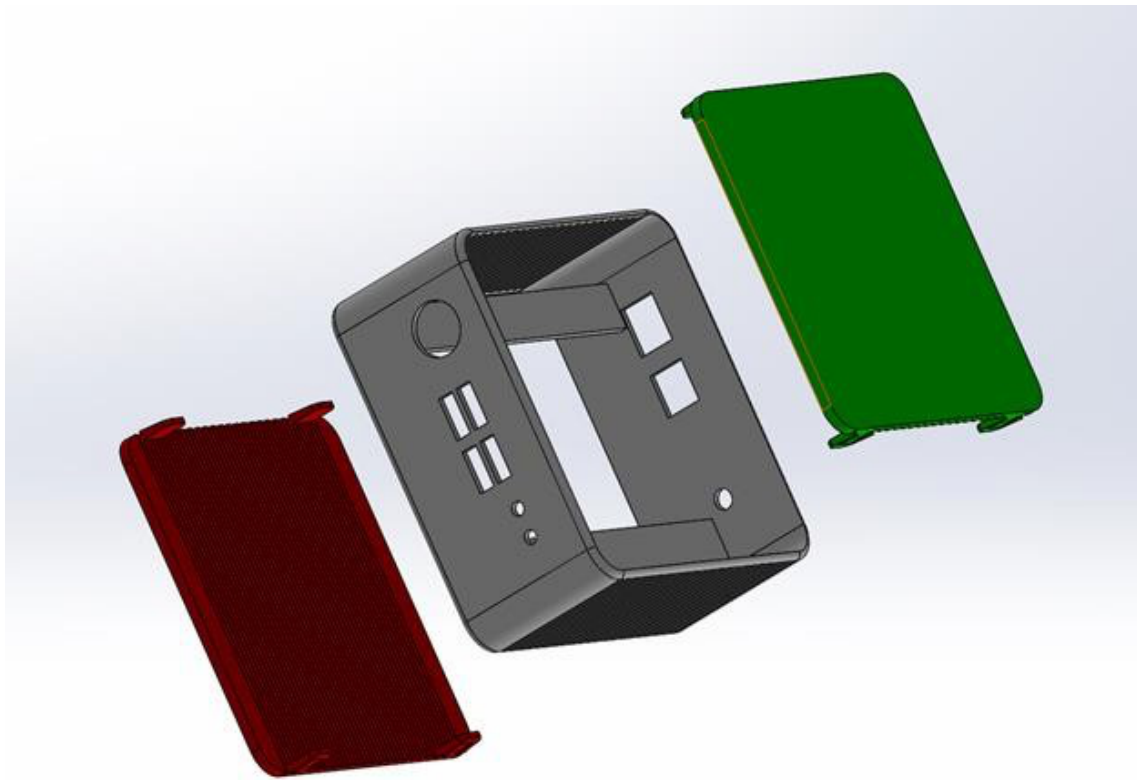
3D exploded view of the theoretical product 理論產品的 3D 分解圖
